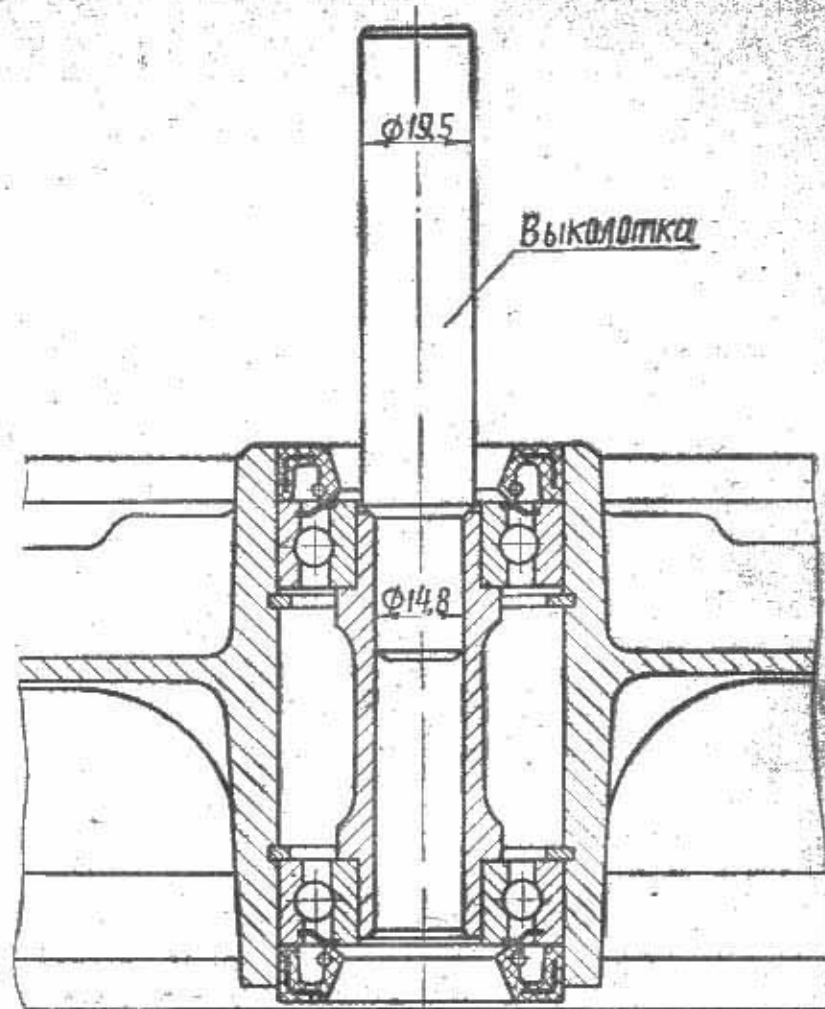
Выпрессовка подшипников и сальников из ступицы колеса.
